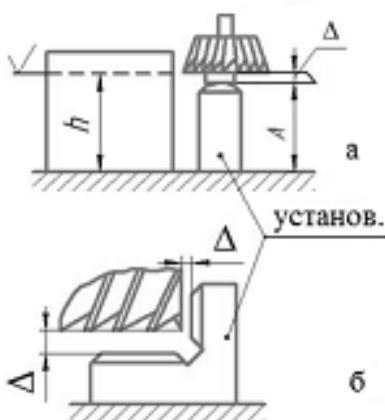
Висотний (а) та кутовий (б) установи для фрезерних пристроїв
